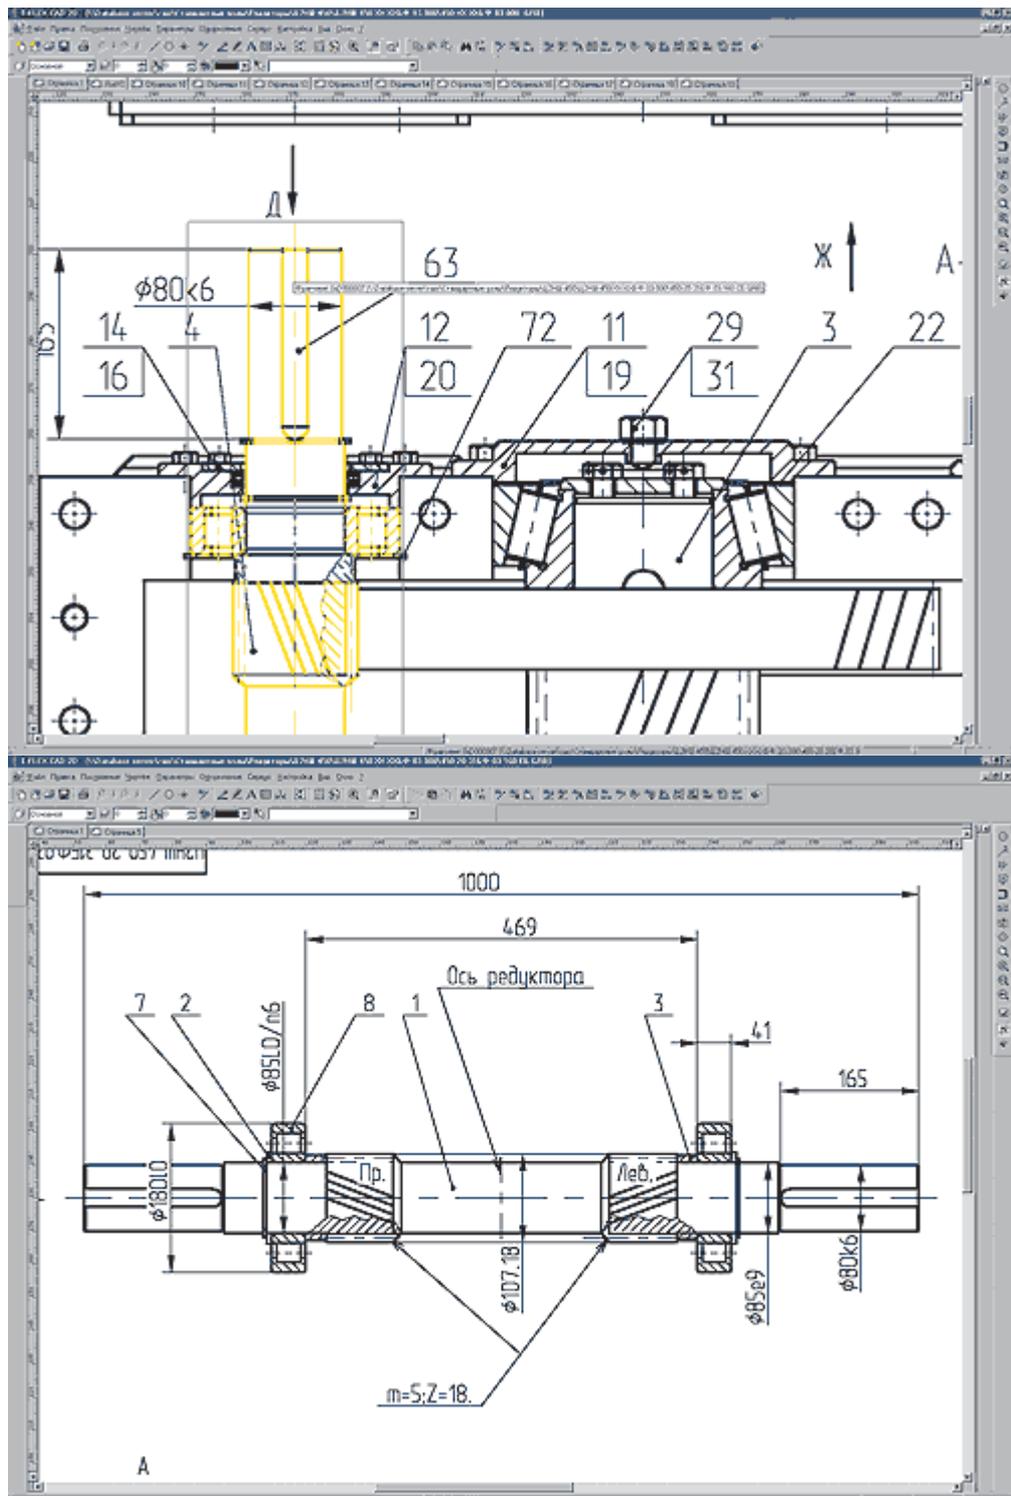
Фрагмент вала с опорами на сборочном чертеже (подсвечен желтым) и рабочий сборочный чертеж вала
